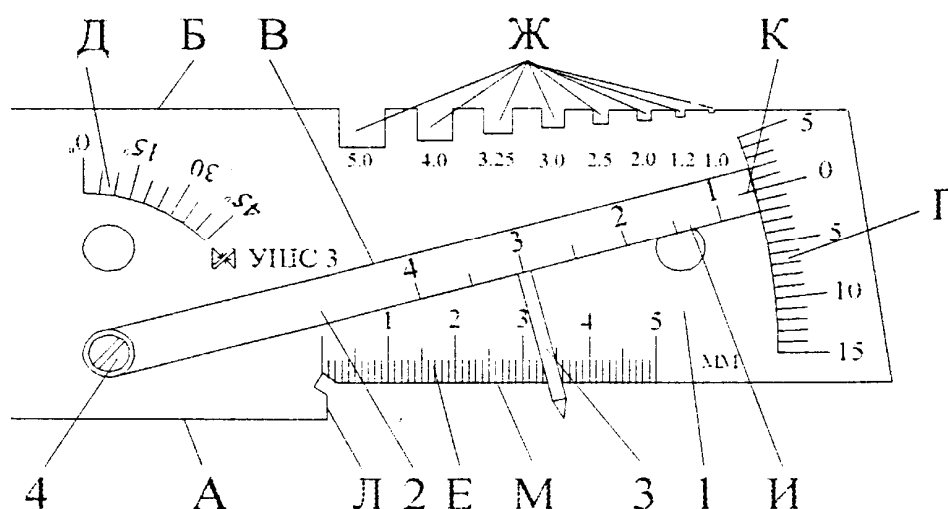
Универсальный шаблон сварщика УШС-3: 1 – основание; 2 – движок; 3 – указатель; 4 – ось; А, Б, В – установочные плоскости; Л – торцовая грань; М – продольное ребро линейки со шкалой Е для измерения величин притупления и ширины шва; Г – шкала для измерения высоты усиления шва; К – риска-индекс для снятия отсчета по шкале Г; Д – шкала для измерения углов скоса кромок; Ж – пазы для измерения диаметров электродов; И – шкала для измерения величины зазора
